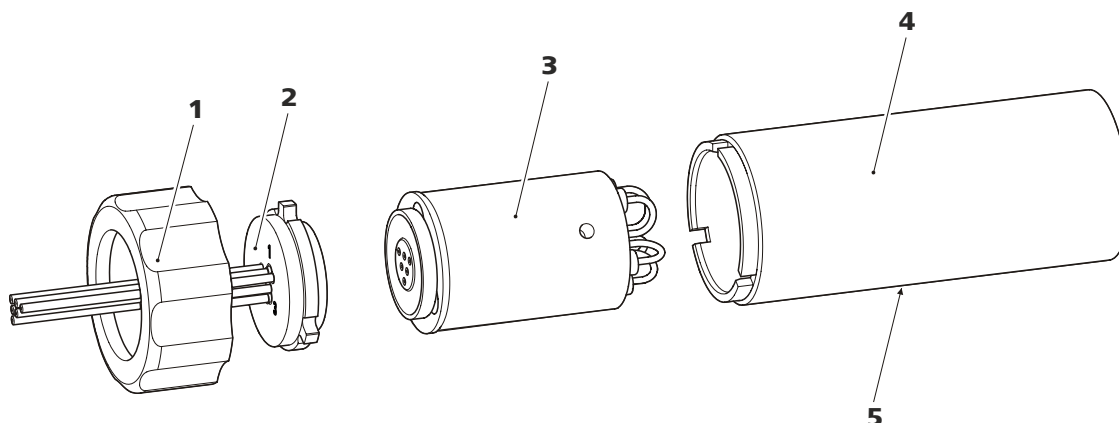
Componentes del Metrohm Suppressor Module (MSM)
